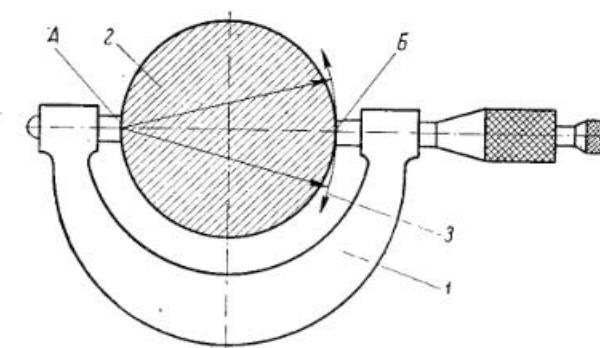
Пример обмера шейки коленчатого вала микрометрической скобой:
